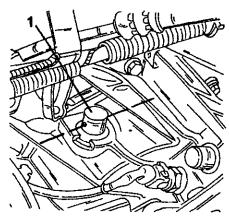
Отверстие под стяжной болт должно располагаться параллельно соединительной поверхности корзины сцепления.
